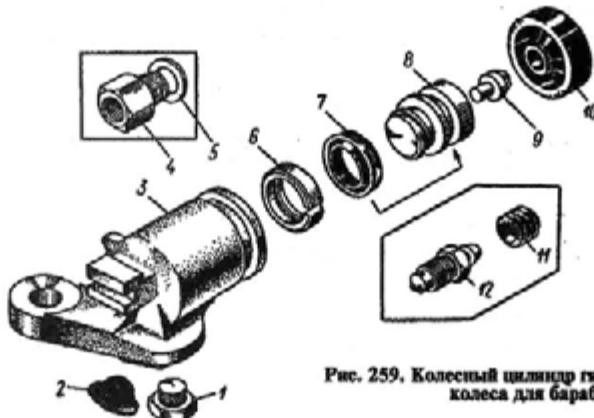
Колесный цилиндр гидропривода тормоза переднего колеса для барабанных тормозов
